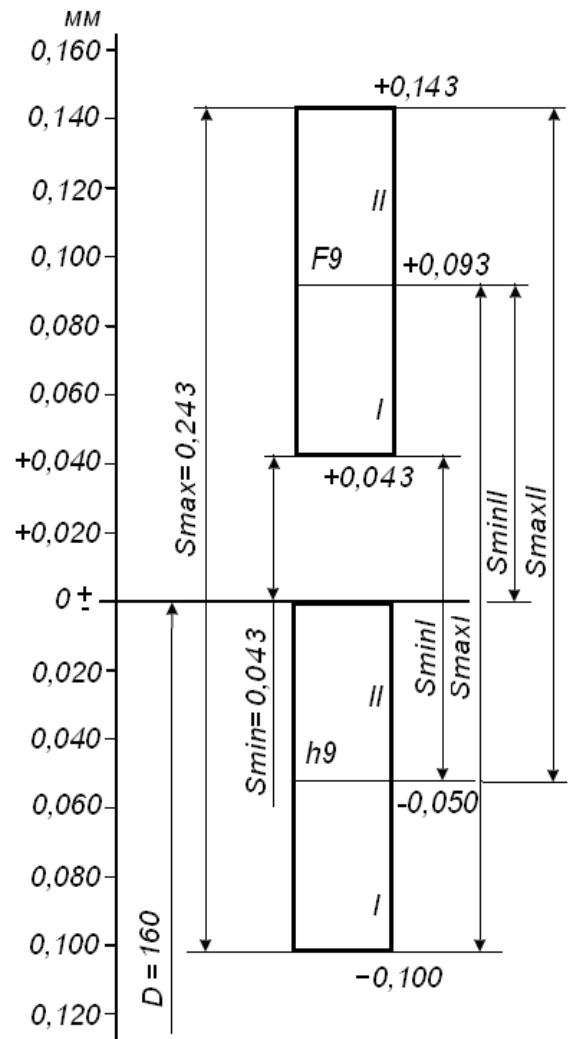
Схема розташування полів допусків з'єднання Ø160F9/h9
